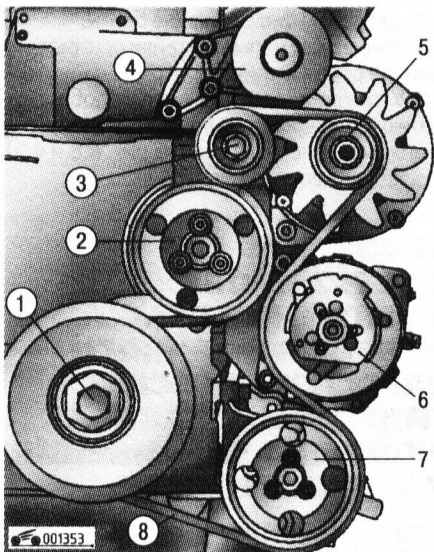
Привод вспомогательных агрегатов: 1 – шкив коленчатого вала; 2 – шкив водяного насоса; 3 – натяжной ролик; 4 – механизм натяжения ремня привода вспомогательных агрегатов; 5 – шкив генератора; 6 – шкив компрессора кондиционера; 7 – шкив гидроусилителя рулевого управления; 8 – ремень привода вспомогательных агрегатов
